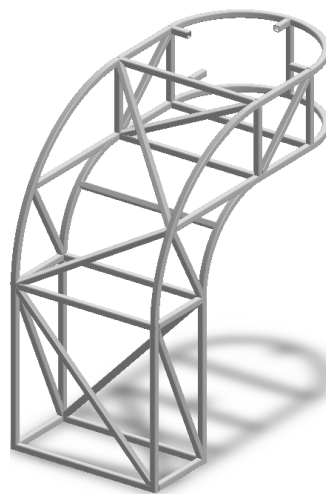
Estructura de la fuente de exterior Fuente: Elaboración propia
